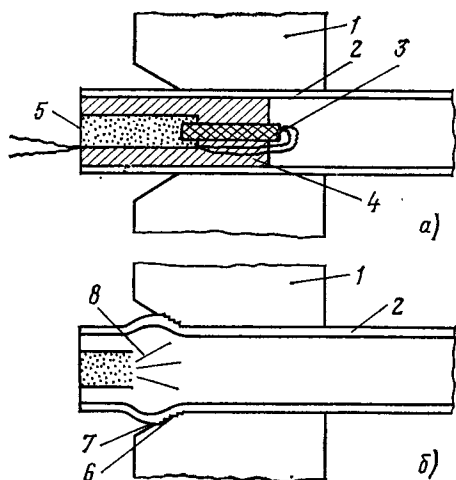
Сварка концов труб с помощью взрыва:
